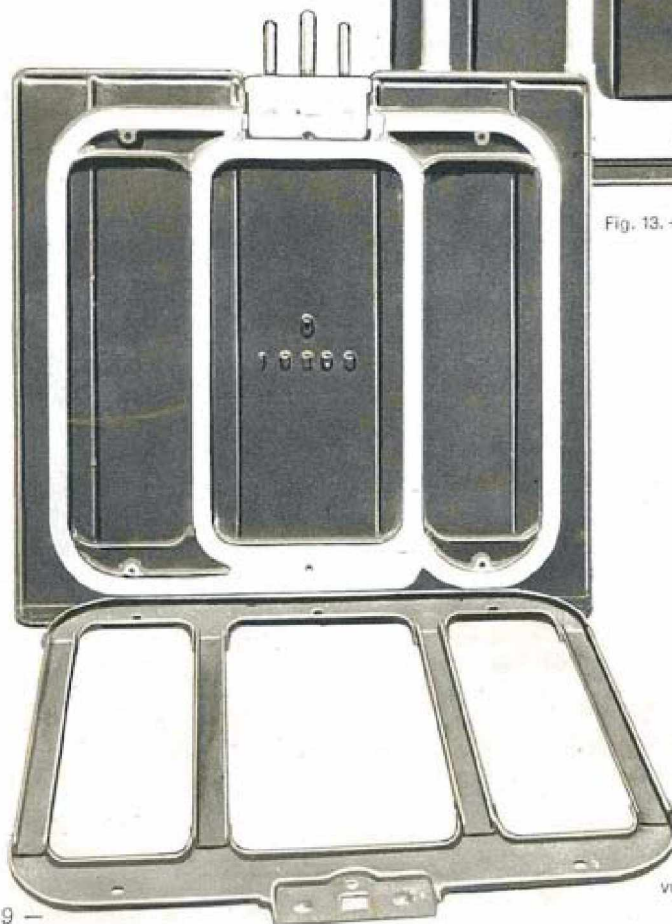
Élément P. 724, vu par en-dessous avec carter ouvert.
